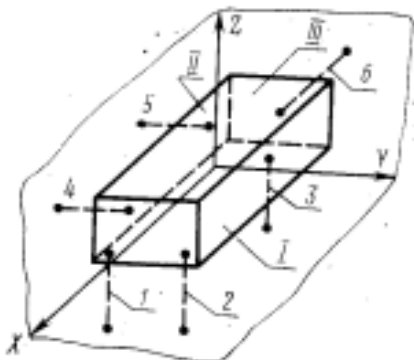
Схема базирования призматической детали: 1-6 – двусторонние связи, I, II, III – базы детали
